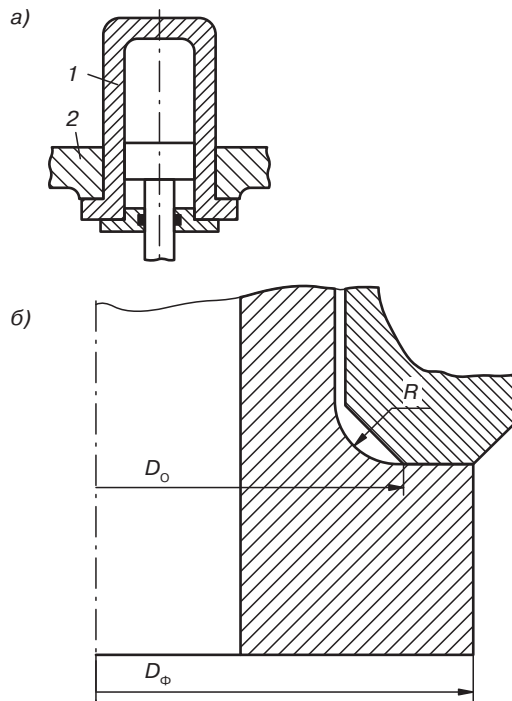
Схема опорного бурта гидроцилиндра: а — схема цилиндра; б — место соединения цилиндра и плиты
